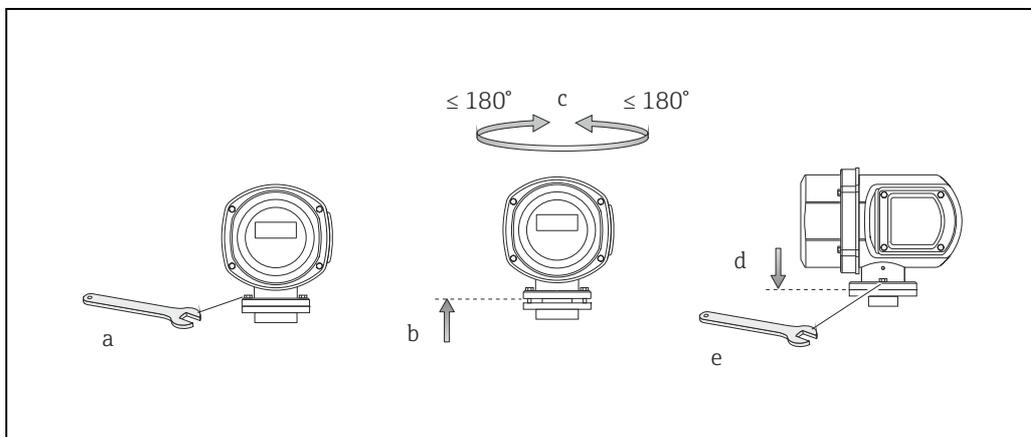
Поворот корпуса преобразователя из нержавеющей стали (полевой корпус из нержавеющей стали)
